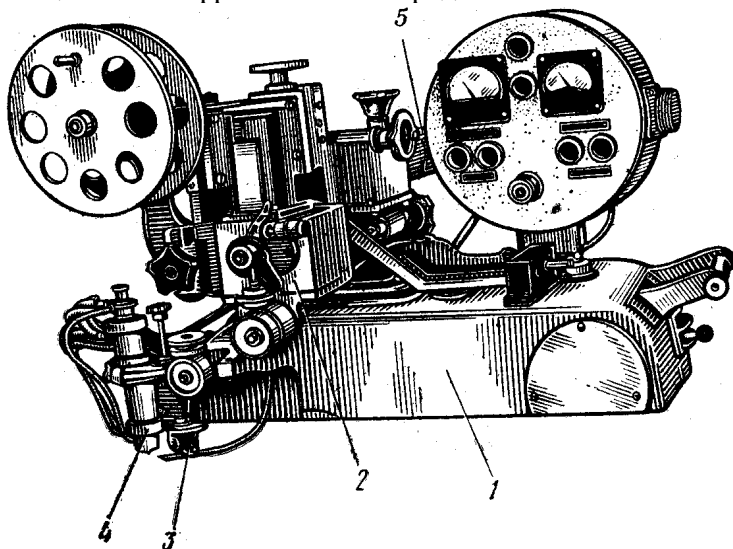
Сварочный трактор АДСВ-2:
